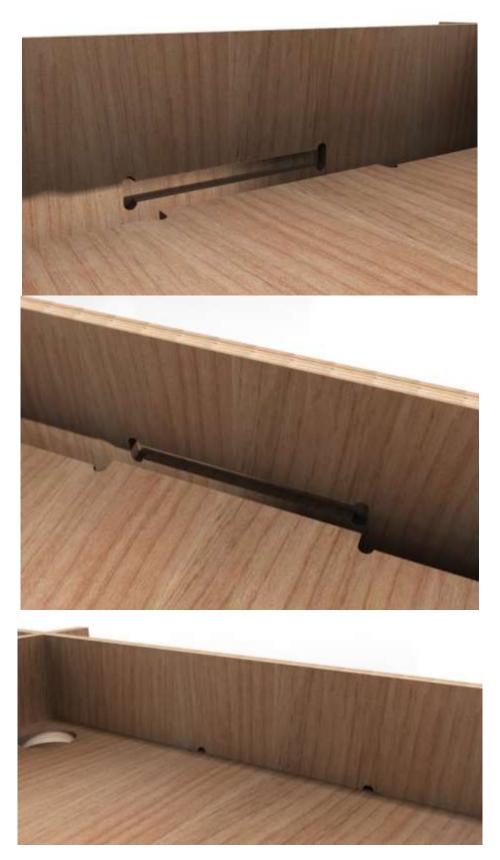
Detalle de montaje de una balda II. Imagen propia.
